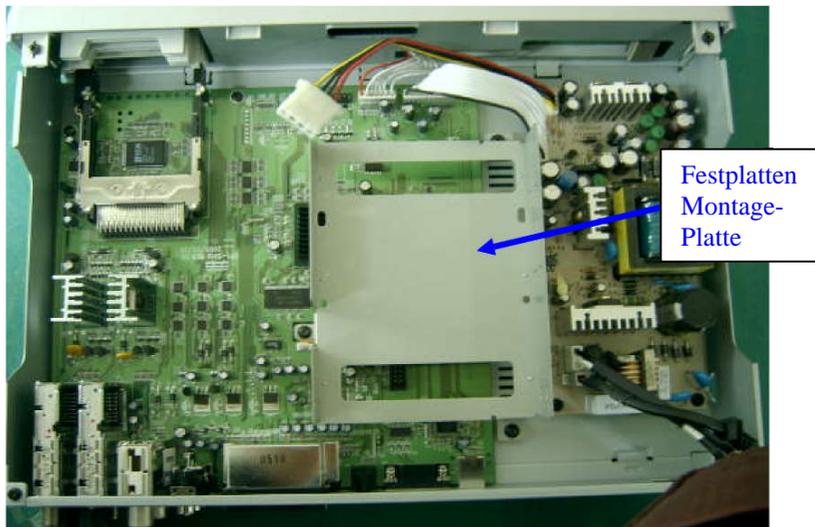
> Innenansicht des Receivers mit der Festplatten-Montageplatte
